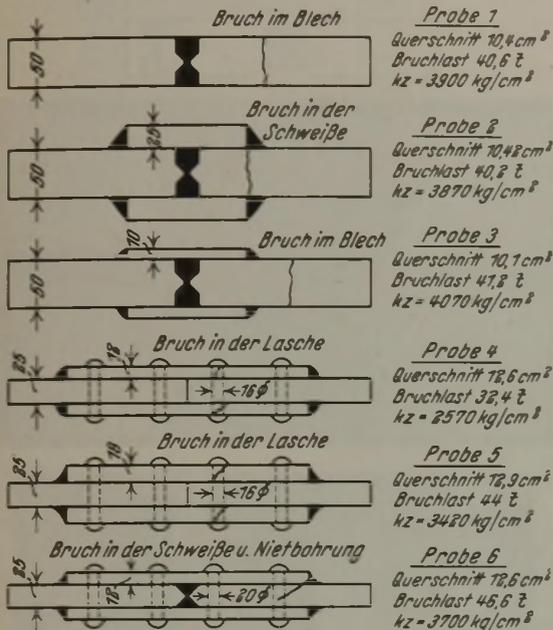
Schweißproben. Werkstoff für alle Proben: St 38.
